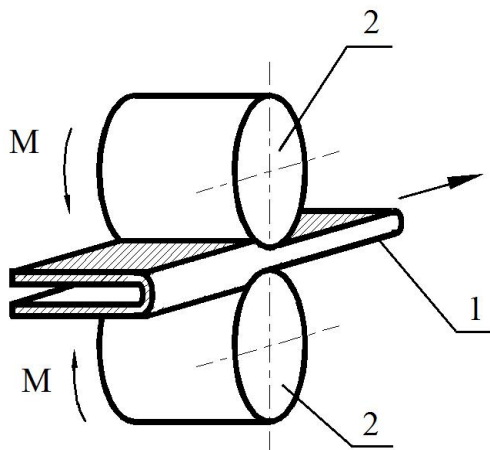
Испытание методом обкатки предварительно согнутой заготовки в цилиндрических роликах: 1 – прокатываемая заготовка, 2 – цилиндрические валки
